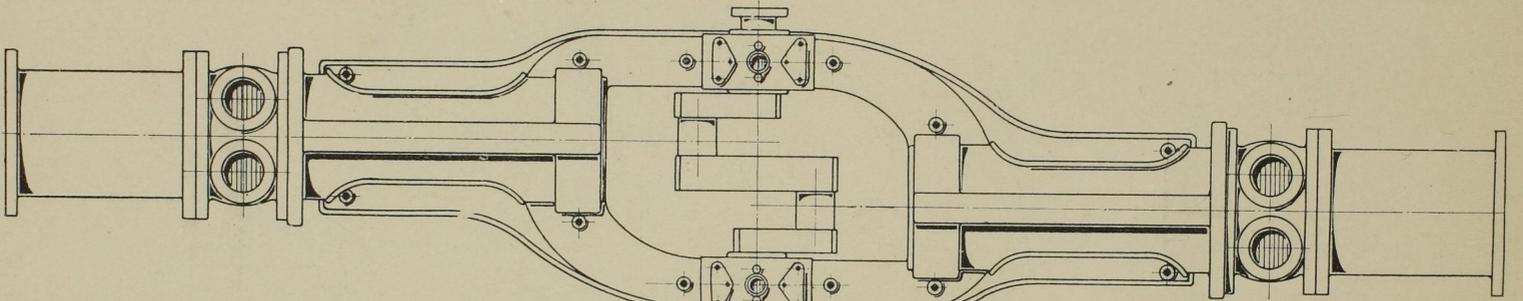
Seitenansicht der Gebläsemaschine und Rückansicht des Windcylinders. Masst. 1:60.
